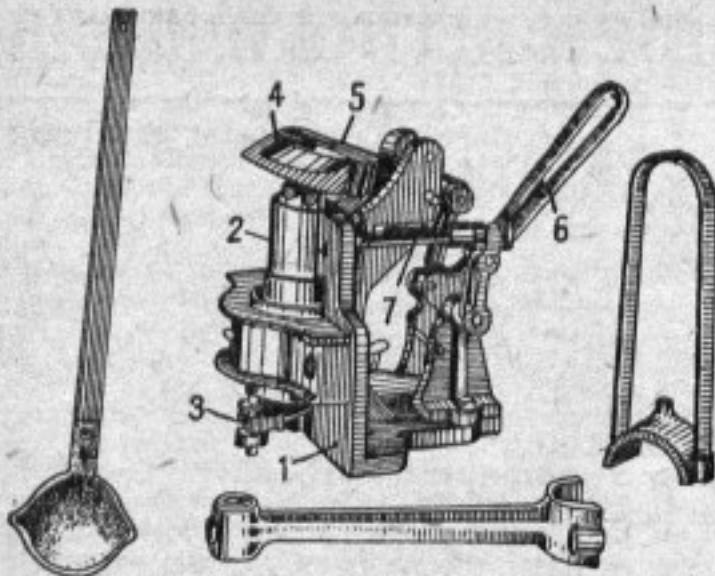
Прибор для заливки шатунных подшипников и крышек коренных подшипников
